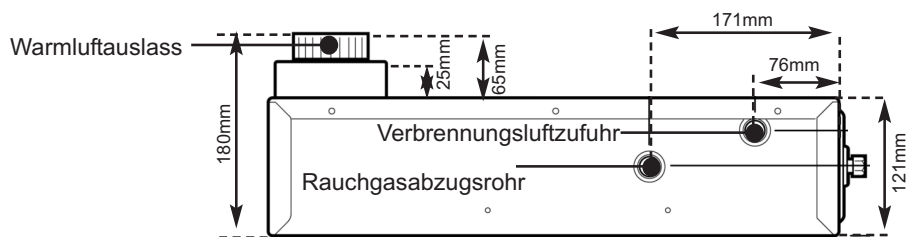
Unterbodenmontage - Seitenansicht - SH2211 oder SC2211
